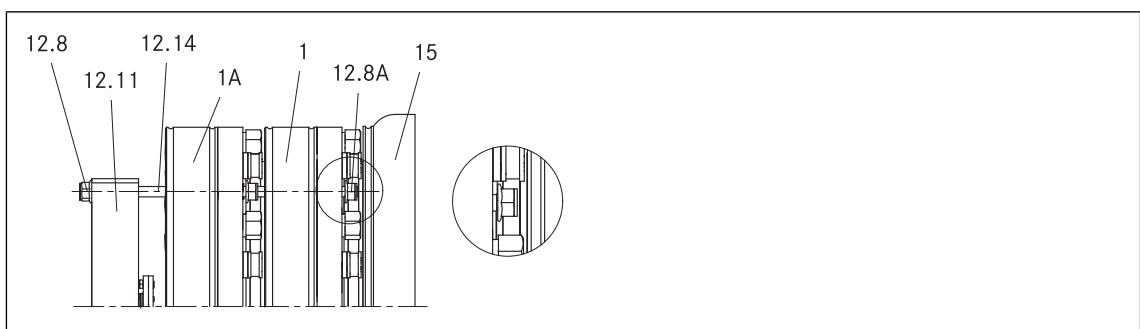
Vormontage der Bremse mit Handlüftung am Motor
